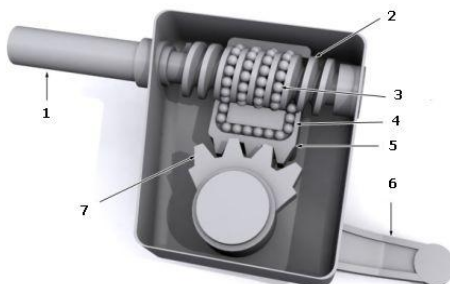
Схема рульового механізму типу „гвинт-кулькова гайка”
